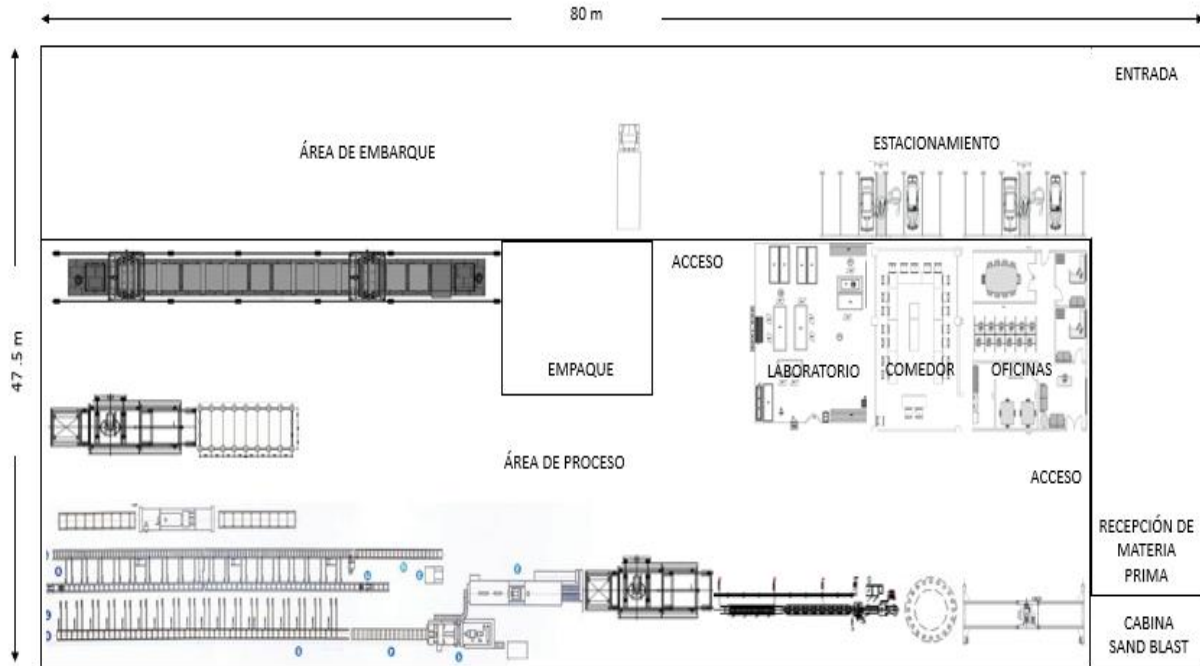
Plano de la planta de perfiles donde se representa la superficie total de la planta y su distribución de cada área.
